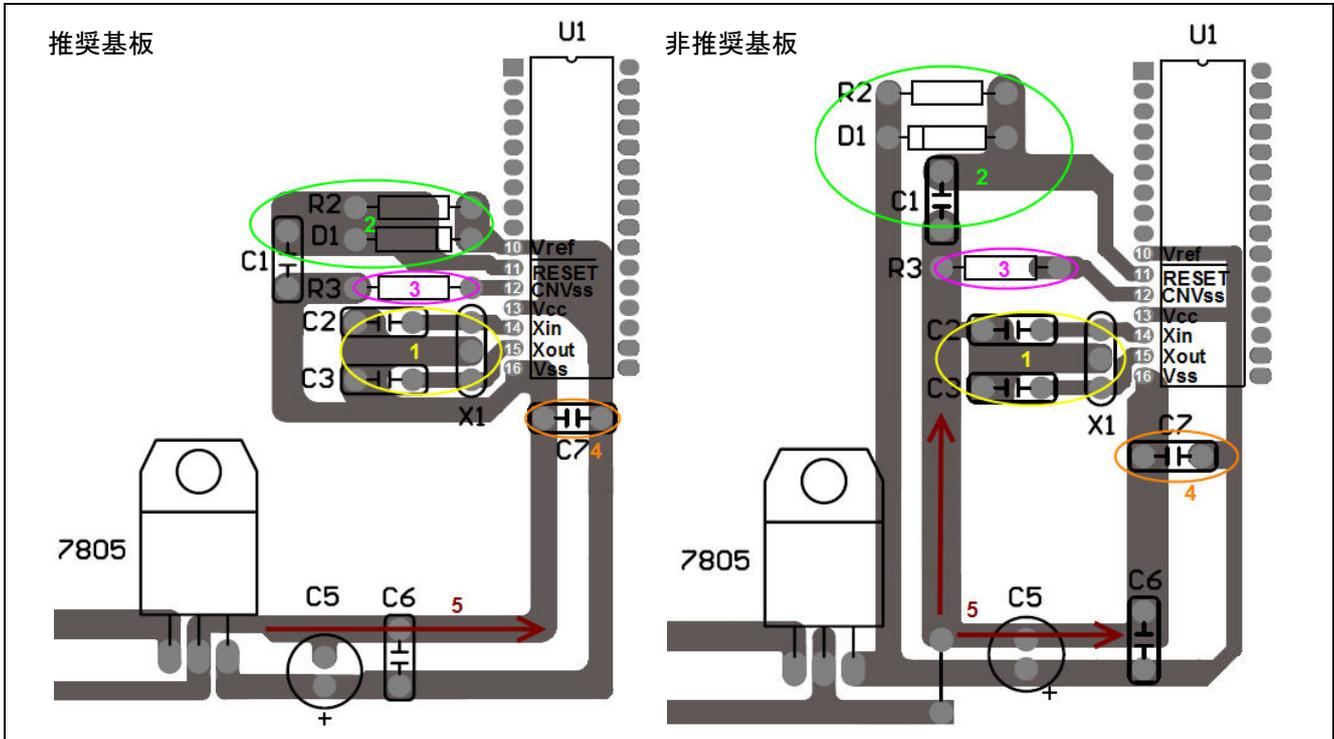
推奨 PCB レイアウト (左) と非推奨 PCB レイアウト (右)
